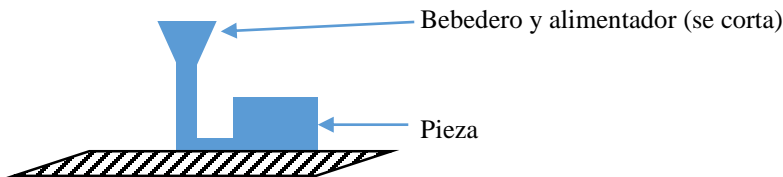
Se debe dejar que la pieza se enfríe, después se retira el molde.
